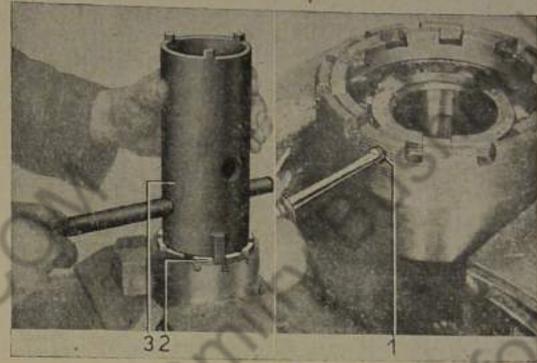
Schrägkugellager aus Einstellbuchse ausbauen
